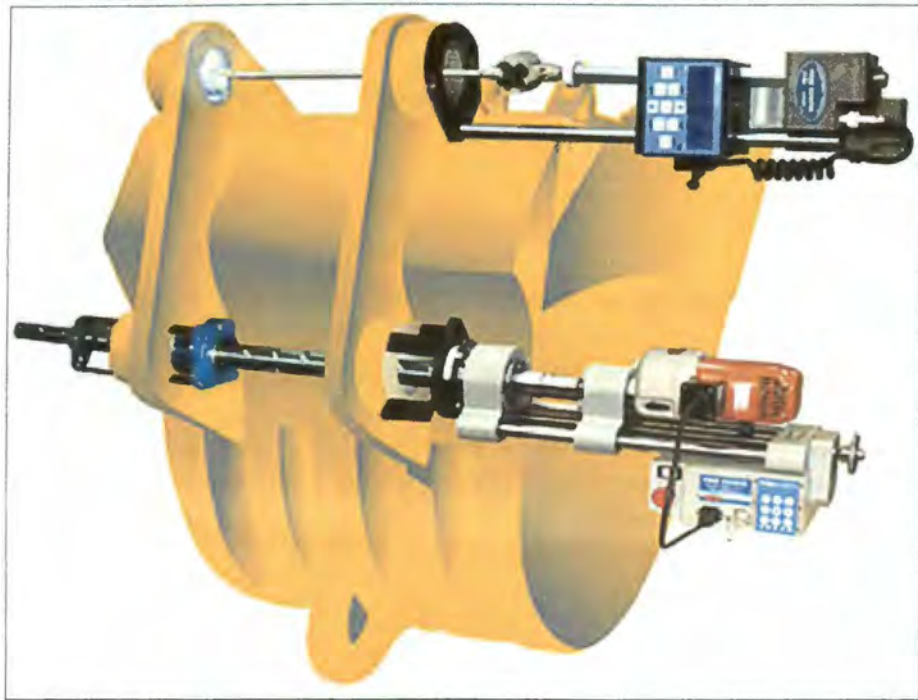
Barrenadora y soldadora instaladas en cucharon
